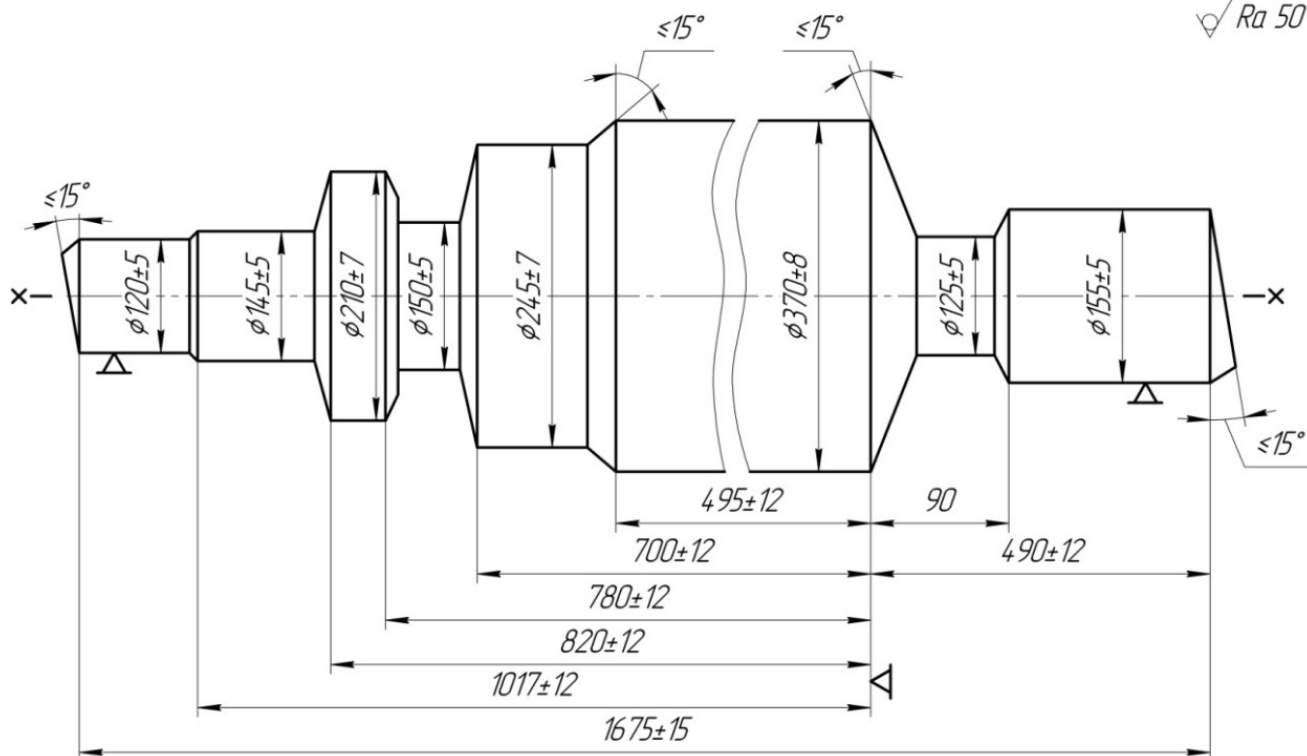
Заготовка, що виготовлена ковкою на пресі
